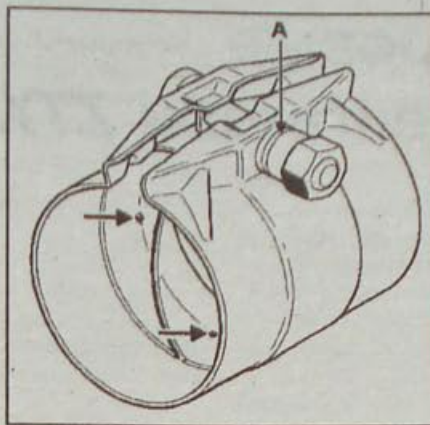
Ремонтный патрубок системы выпуска отработавших газов: А – канавка, определяющая момент затяжки гайки
